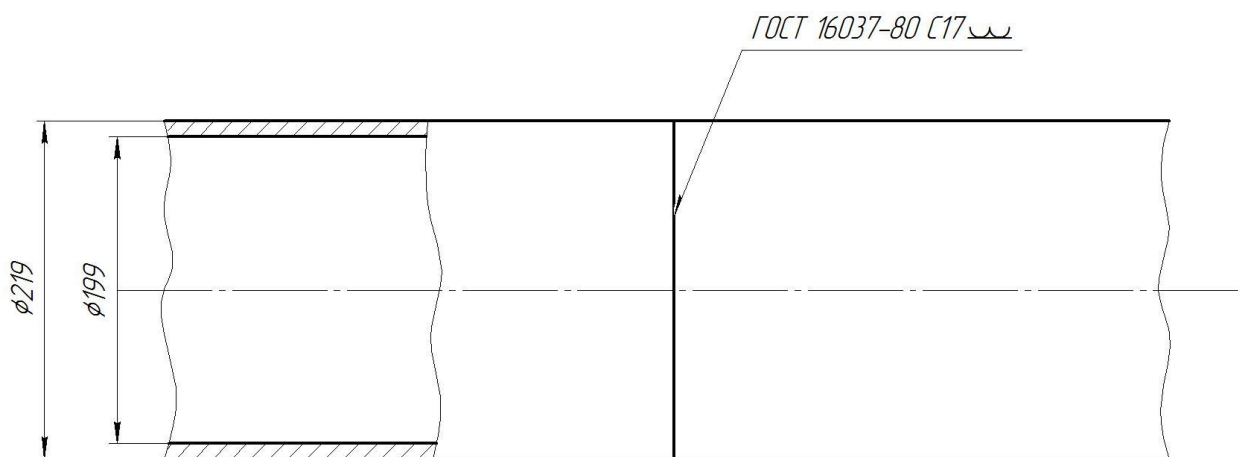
Подготовка кромок и сварной шов соединения С17 по ГОСТ 16037–80
